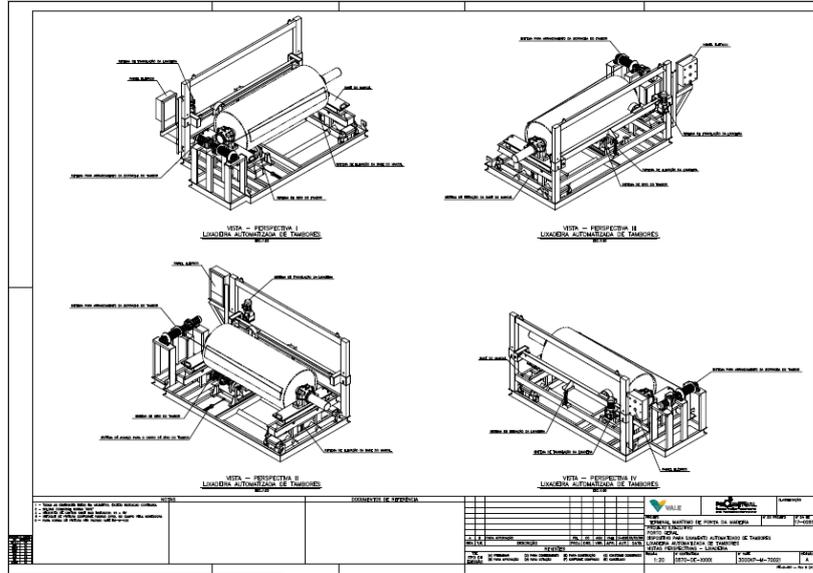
Desenho técnico padrão da engenharia contendo vistas do dispositivo
